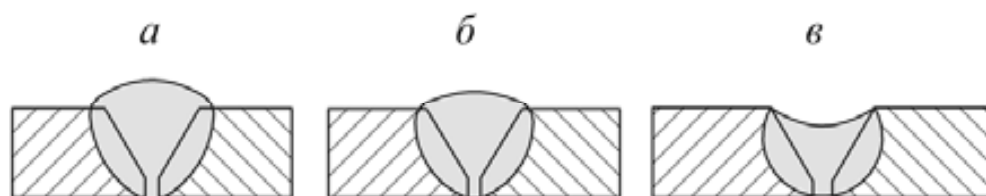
Форма сварных стыковых швов: *а* – выпуклый сварной шов; *б* – нормальный шов; *в* – вогнутый
